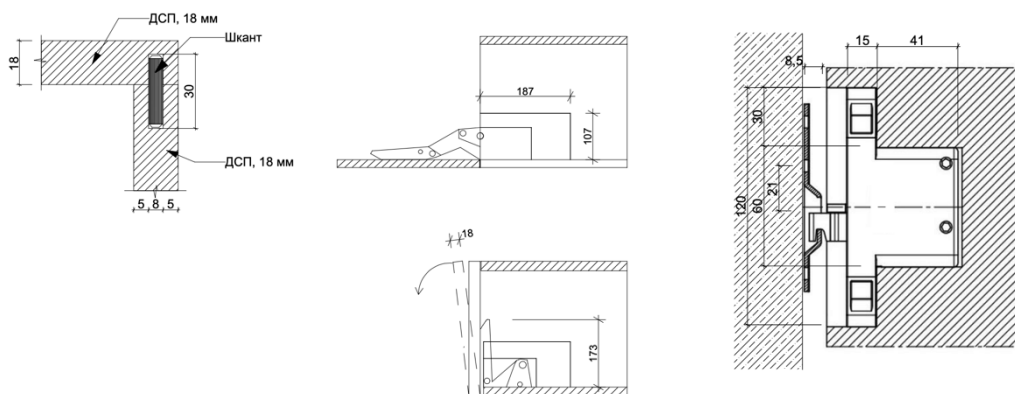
Вузол з'єднання ДСП дерев'яним шкантом, схема відкриття системи НК top та схема кріплення стелажу до стіни
